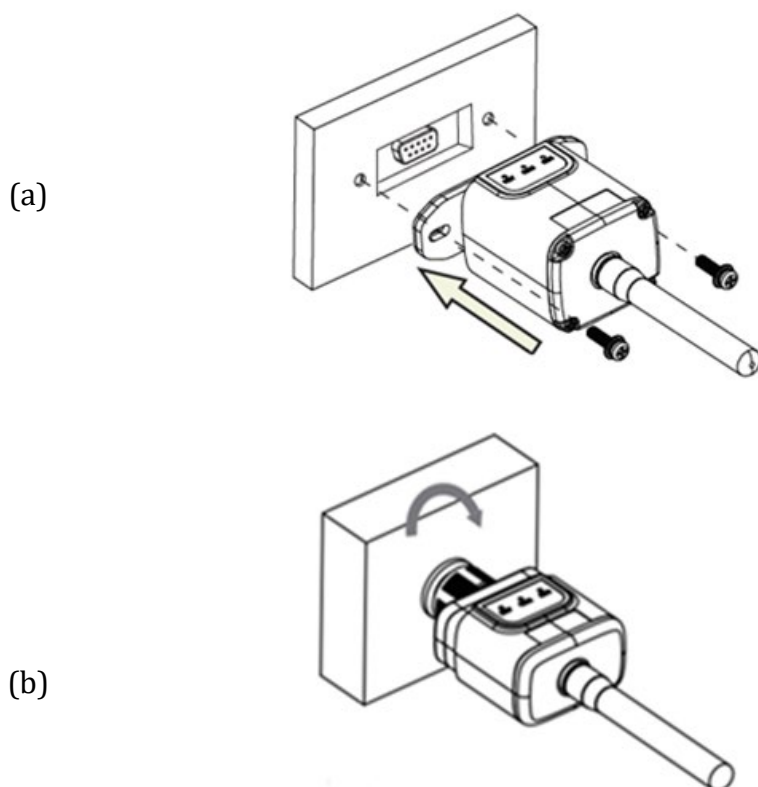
Inserimento e fissaggio dell'adattatore 4G
